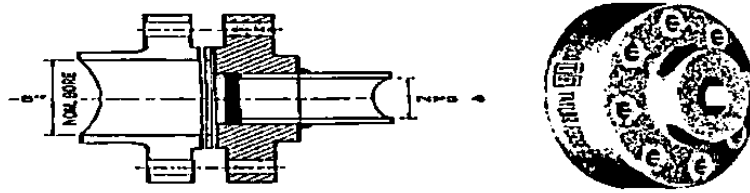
Flange* Jenis WN (*Welding Neck*)
